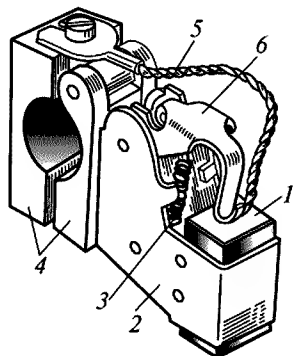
Щеткодержатель: 1 — щетка; 2 — корпус (обойма) щеткодержателя; 3 — пружина; 4 — зажимы; 5 — медный шунт; 6 — нажимная планка
